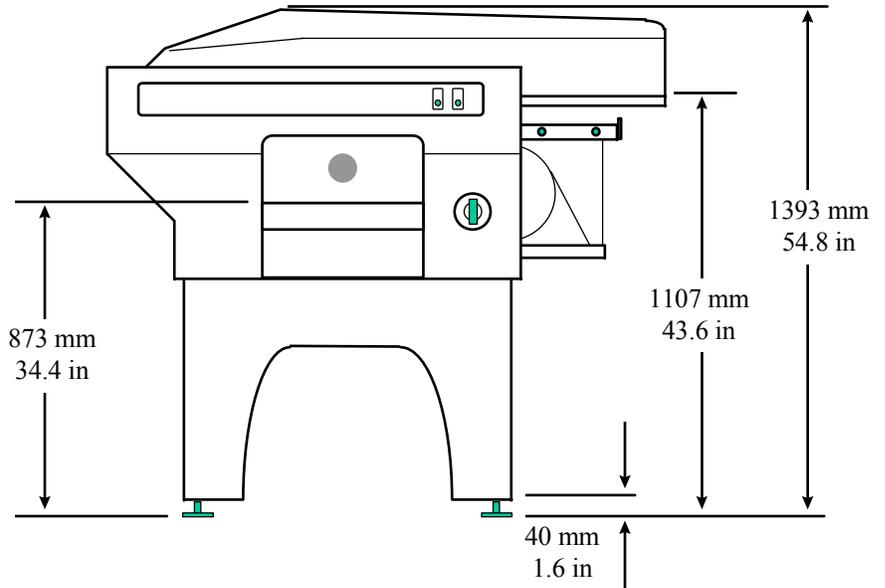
Dimensions SOLO™ XL (Vue latérale)
